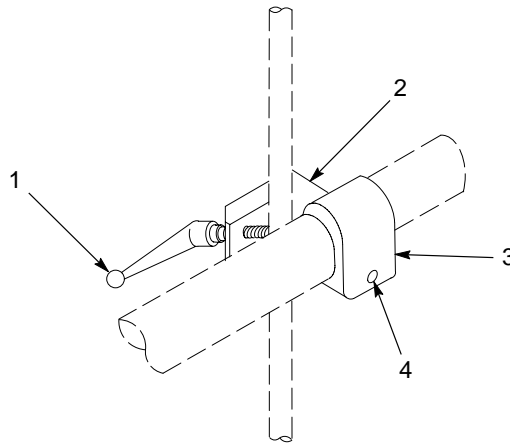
Conjunto de barra de pistola estándar para pistolas para montaje en tubo
